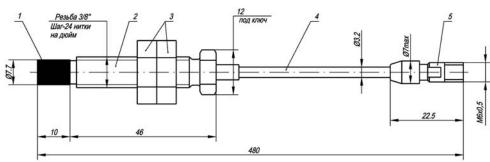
Преобразователь вихретоковый ИЦФР.408113.021 (код ПВ17): 1 — наконечник; 2 — корпус; 3 — гайка; 4 — кабель; 5 — розетка СР-50-106ФВ
